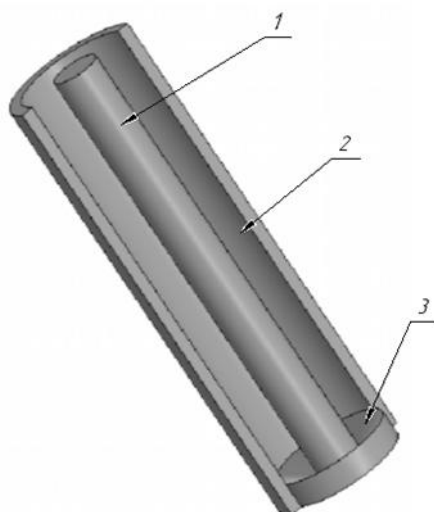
Трёхмерная модель заготовки после кольцевого сверления:
